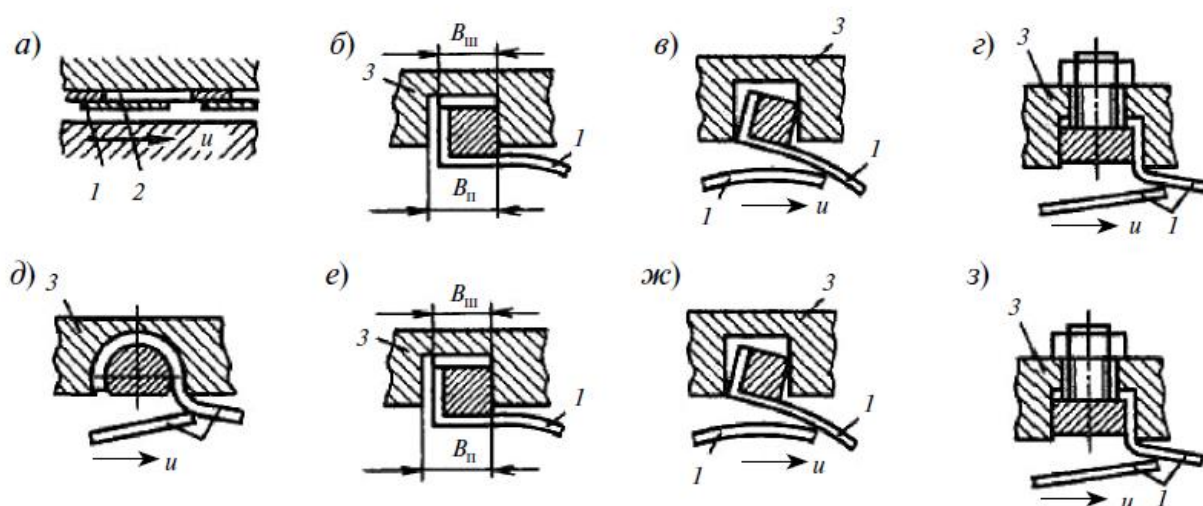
Схемы узла крепления лепестка к корпусу подшипника:
